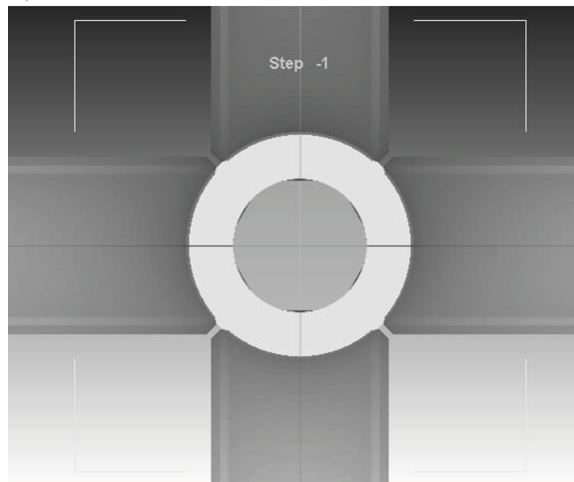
Охват роликами 1 поверхности заготовки 2 (образование огранки)
